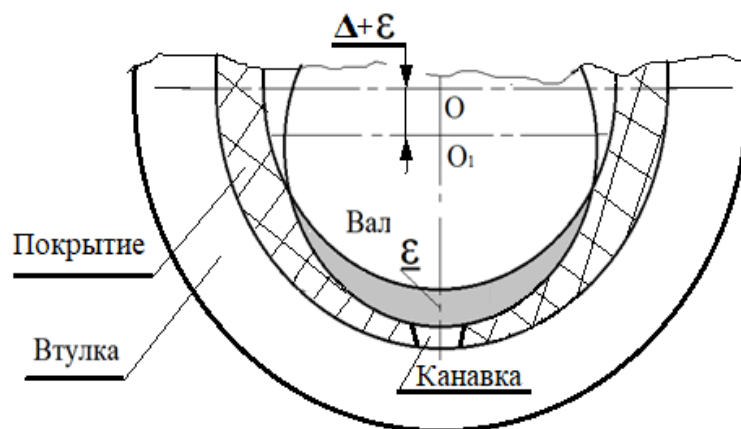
Схема статического металлополимерного трибоконтакта:
